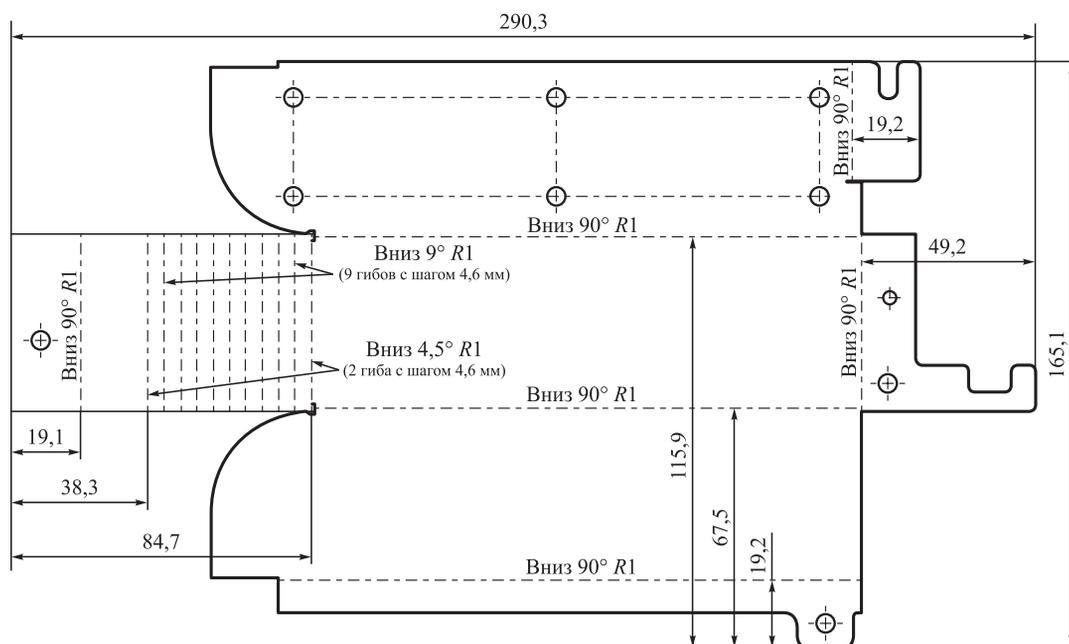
Развернутый вид деформируемой заготовки бампера двери стерилизатора с указанием линий изгиба
